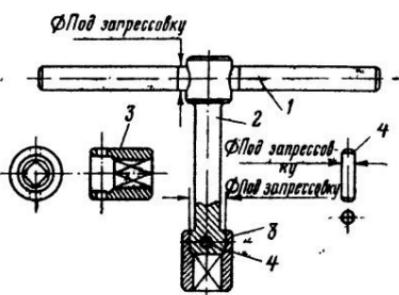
59. Торцевый ключ для резцедержателя токарного станка: 1 — ручка; 2 — стержень; 3 — ключ; 4 — шпилька.
